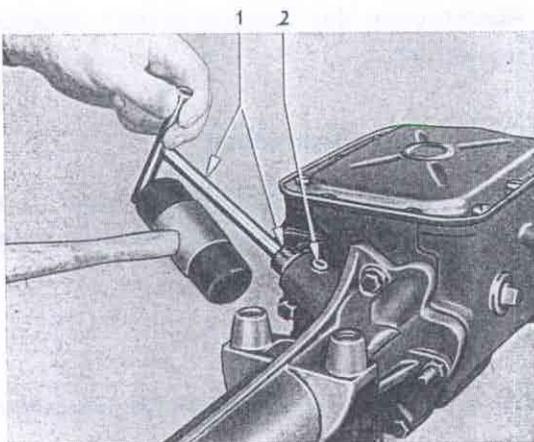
Tachometerantrieb aus Getriebegehäuseverlängerung mit Montagewerkzeug SW-204 herausschlagen
